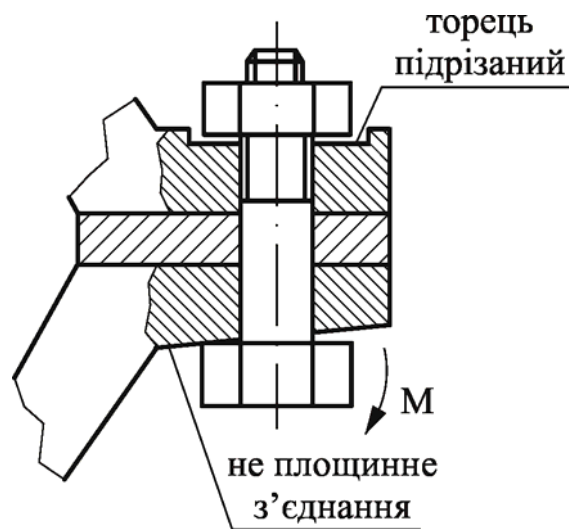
Приклад підготовки полиць для болтового з'єднання.
